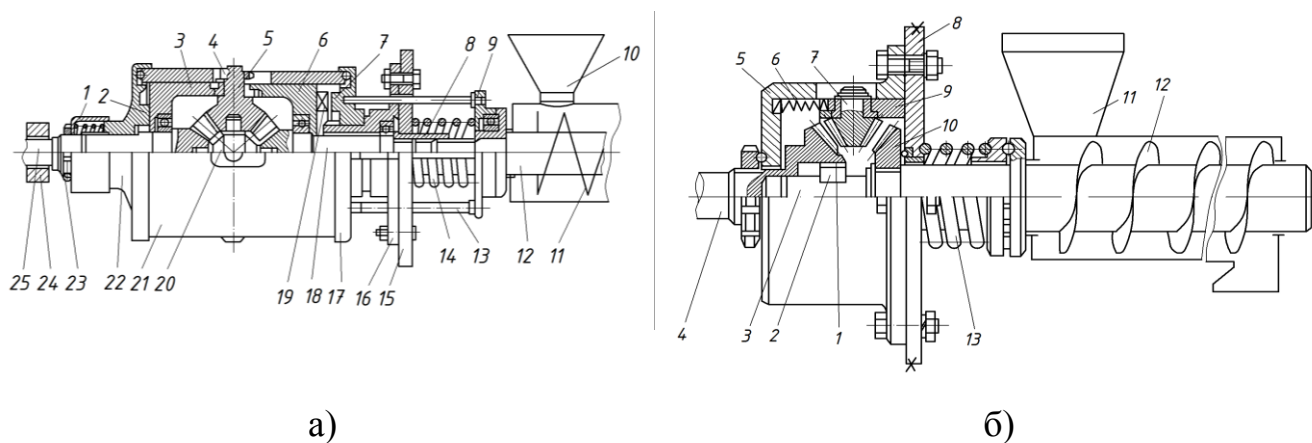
Конструкції реверсивних запобіжних муфт ГК:
